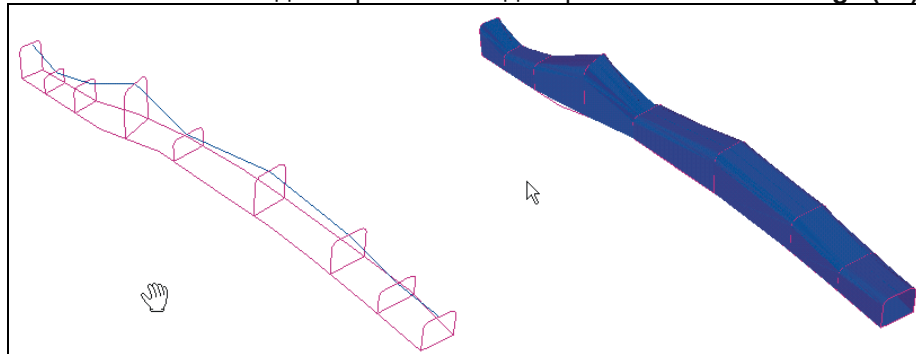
Создание каркаса по контуру подошвы и линии кровли
